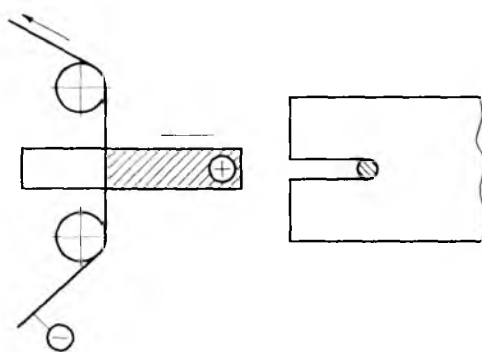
Схема обработки заготовки непрофилированным электродом
